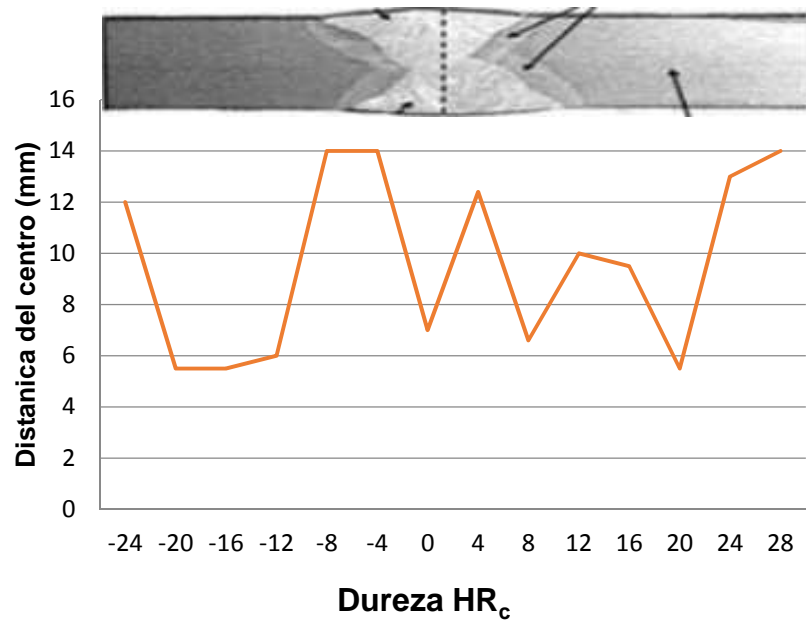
Zonas y distancias de la soldadura ensayadas en durómetro
